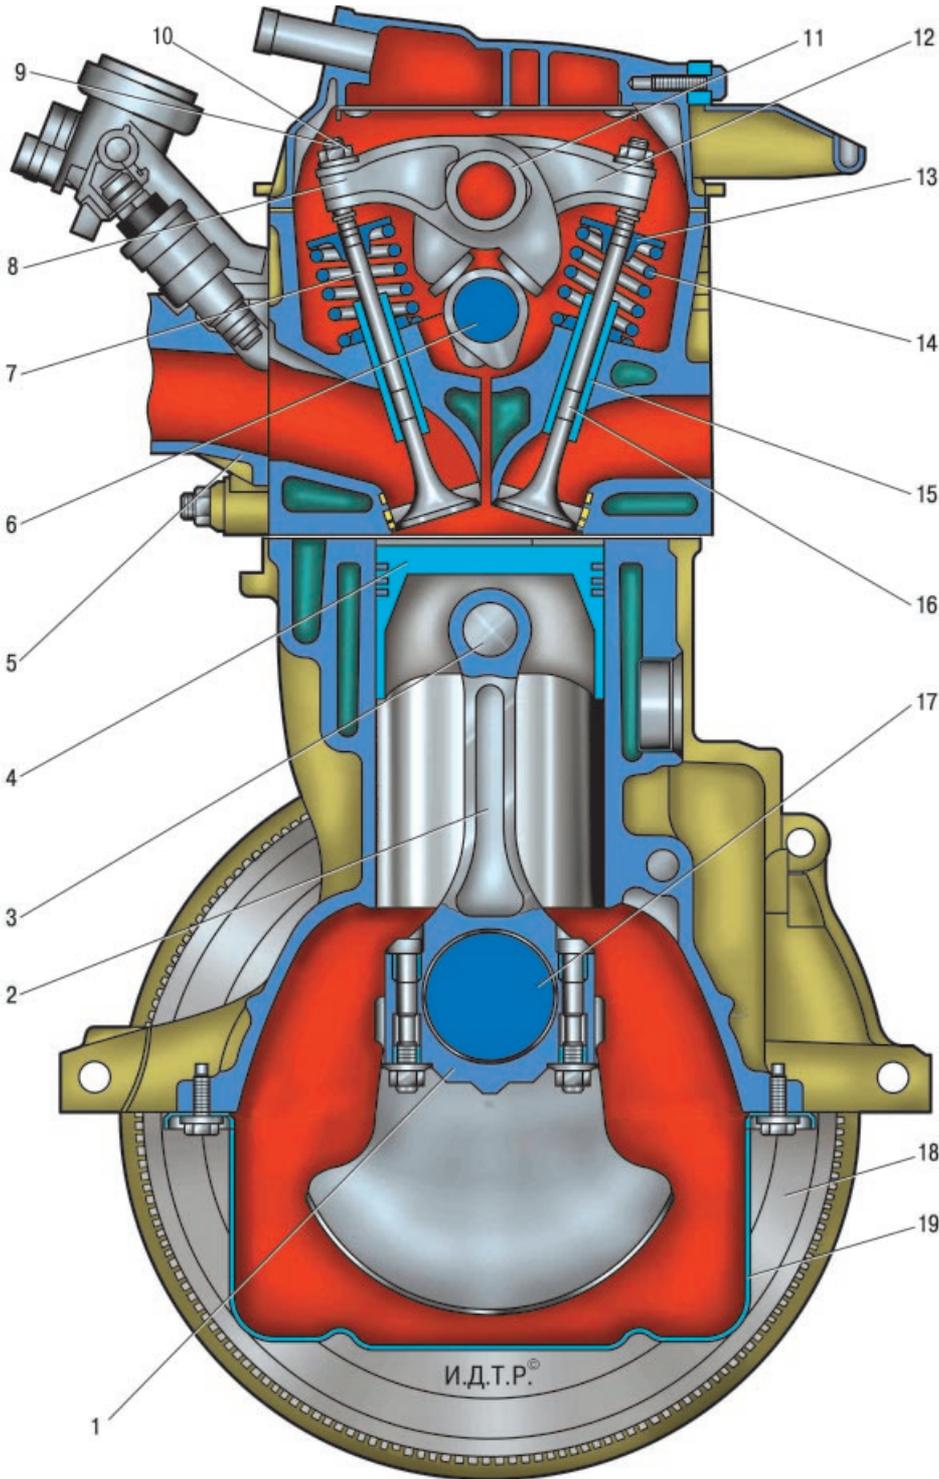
Двигатель K7J (поперечный разрез): 1 – крышка шатуна; 2 – шатун; 3 – поршневой палец; 4 – поршень; 5 – впускная труба; 6 – распределительный вал; 7 – впускной клапан; 8 – коромысло впускного клапана; 9 – регулировочный болт; 10 – контргайка регулировочного болта; 11 – ось коромысел привода клапанов; 12 – коромысло выпускного клапана; 13 – тарелка пружины клапана; 14 – пружина клапана; 15 – направляющая втулка клапана; 16 – выпускной клапан; 17 – коленчатый вал; 18 – маховик; 19 – масляный картер
